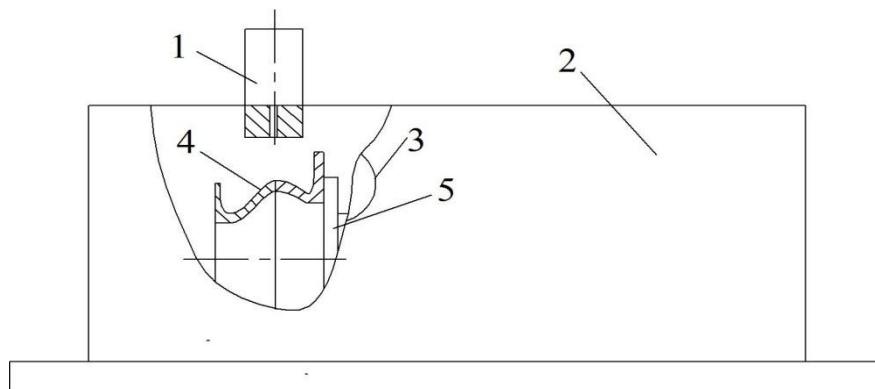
Принципиальная схема установки для электронно-лучевой сварки:
